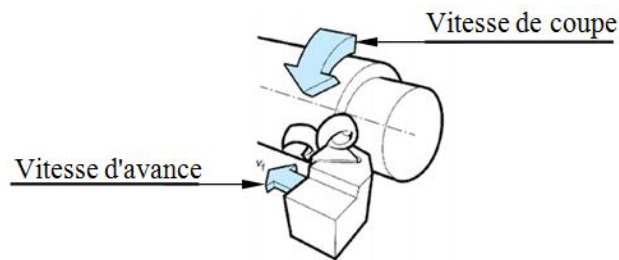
Vitesse de coupe dans l'usinage du tour.
